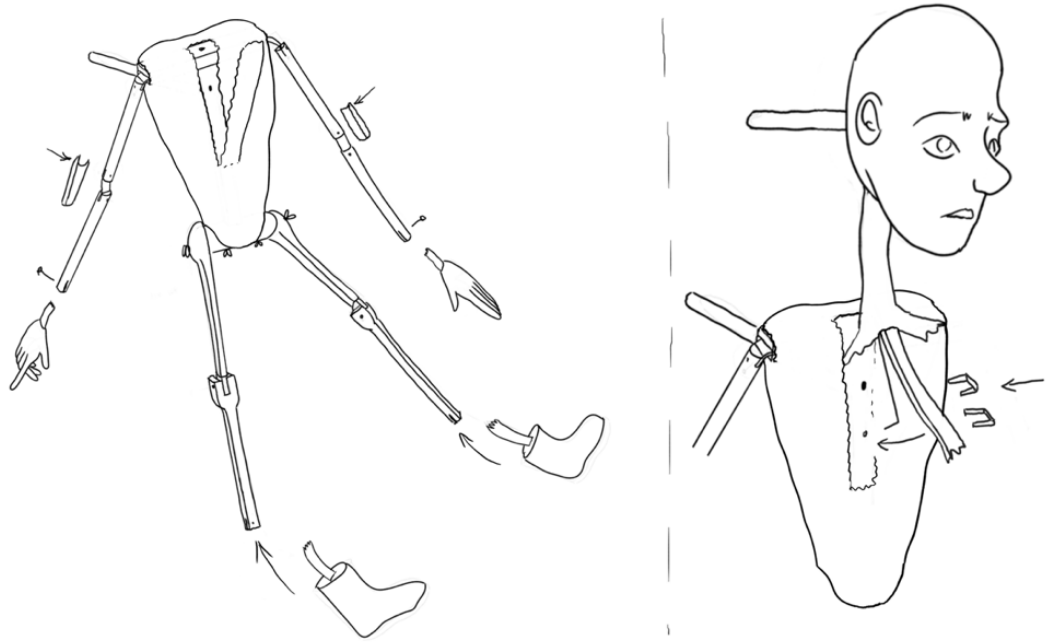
Puurangan kokoaminen nylonnauhalla, pianolangalla ja kuminyöriillä.
